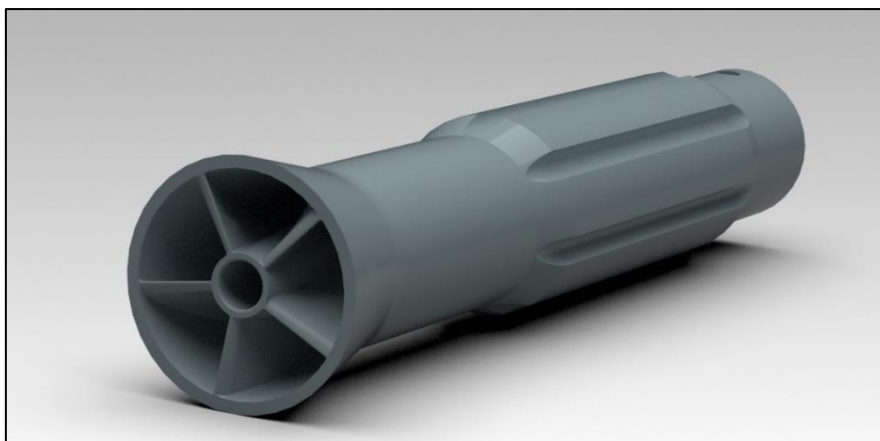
Przykład projektowanego elementu silnika przeznaczony do wydrukowania w metalu
